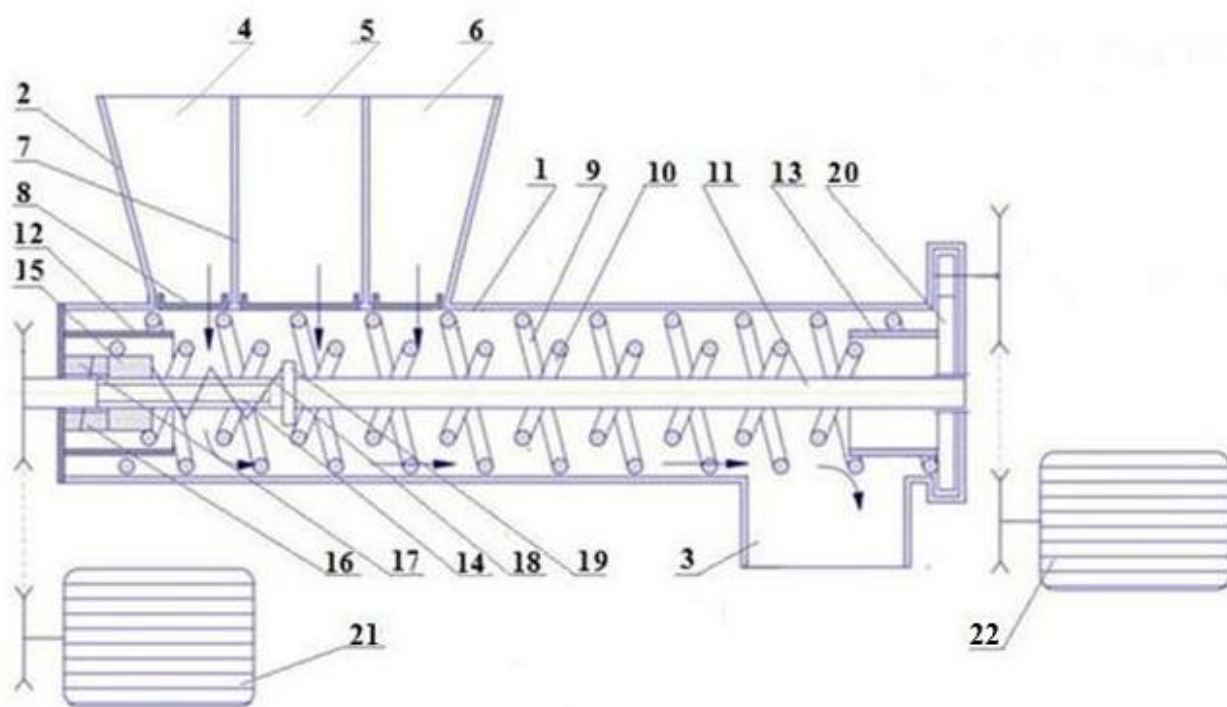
Схема агрегата для приготовления кормов (обозначения в тексте)
